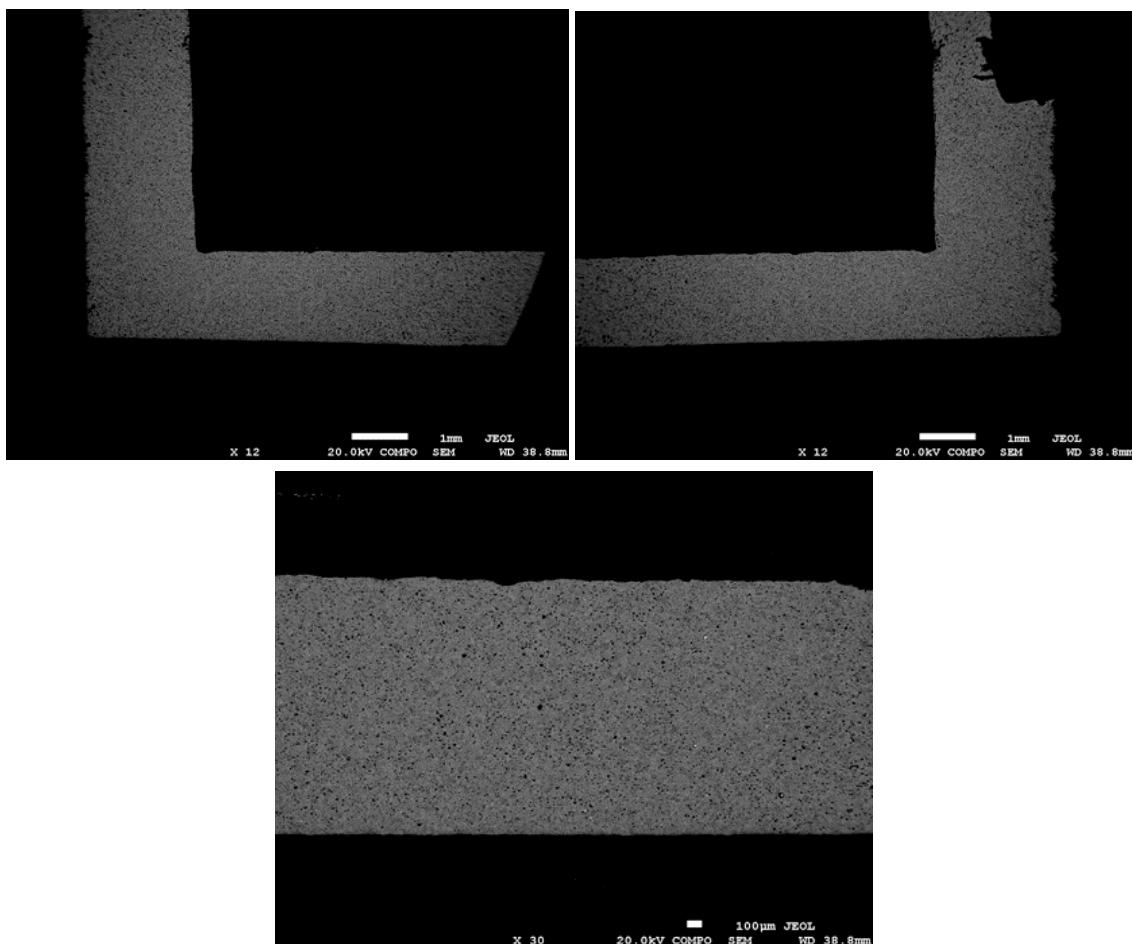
Corte transversal de la pieza 1F con boquilla 0,5mm
